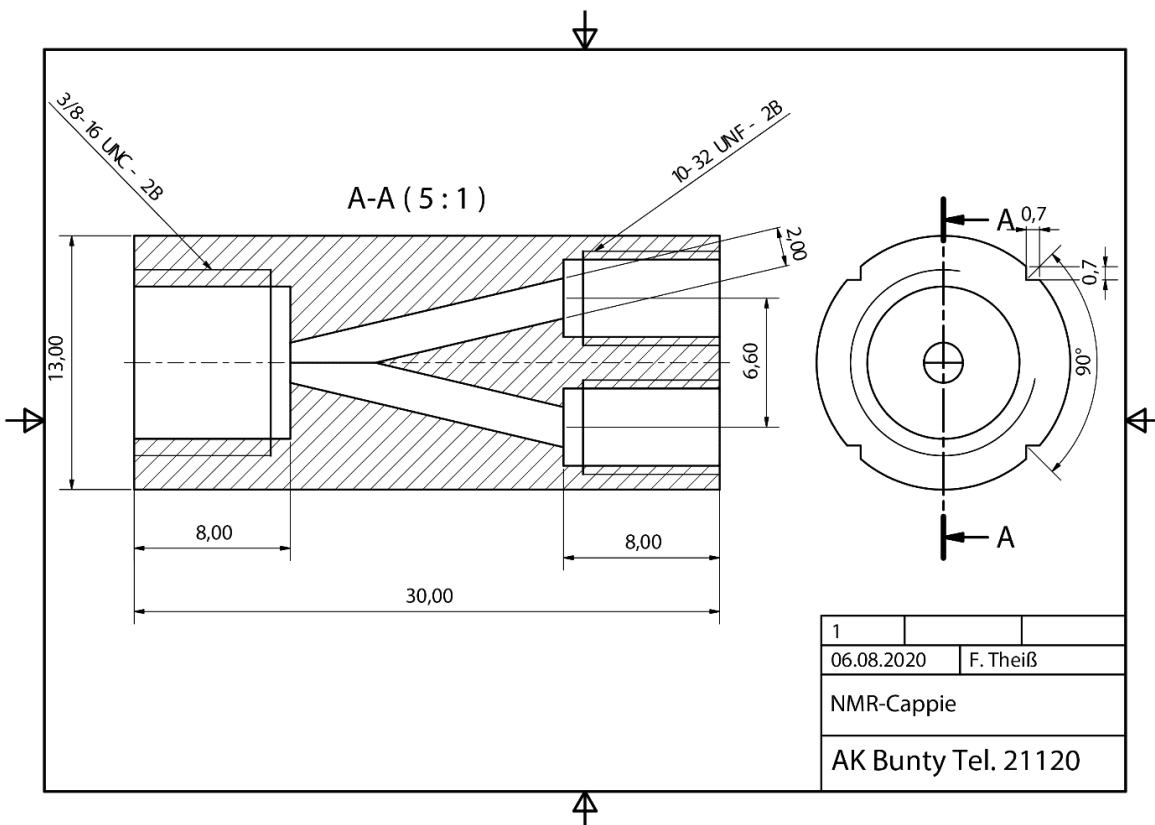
Technische Zeichnung des NMR-Röhrchen-Adapters, mit Längen- und Gewindemaßangaben.
